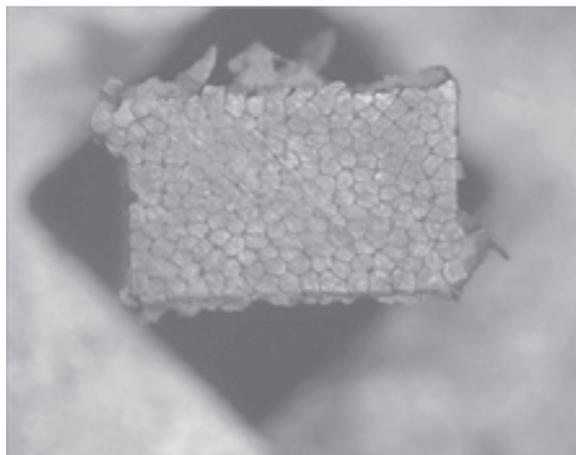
Шлиф в области сварки ПМЛ на установке резистивной сварки WWS1 (Strunk Welding Systems GmbH)
